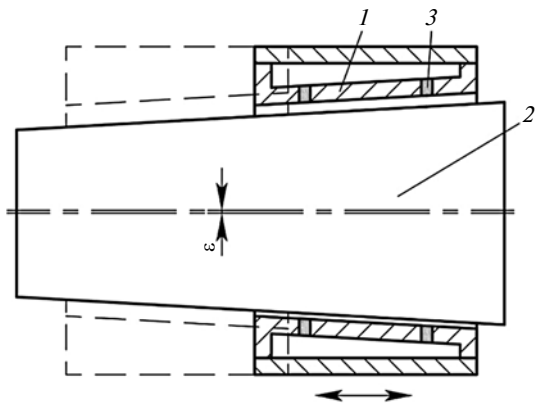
Конструкция газостатической опоры с малой конусностью: 1 — вкладыш подшипника; 2 — шип; 3 — питатель
